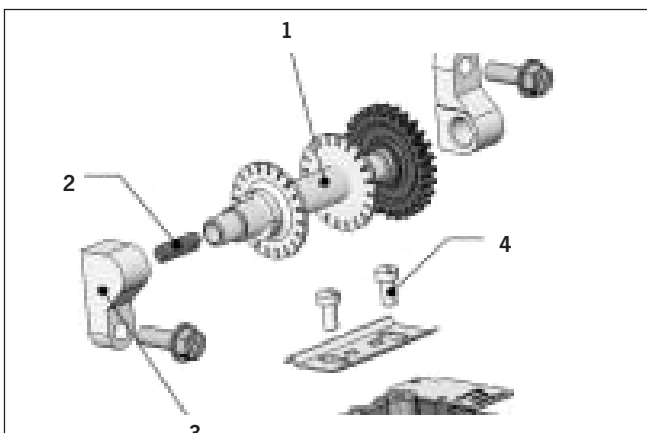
b - Endschalter - Gehäusetypen J bis RRT-2
